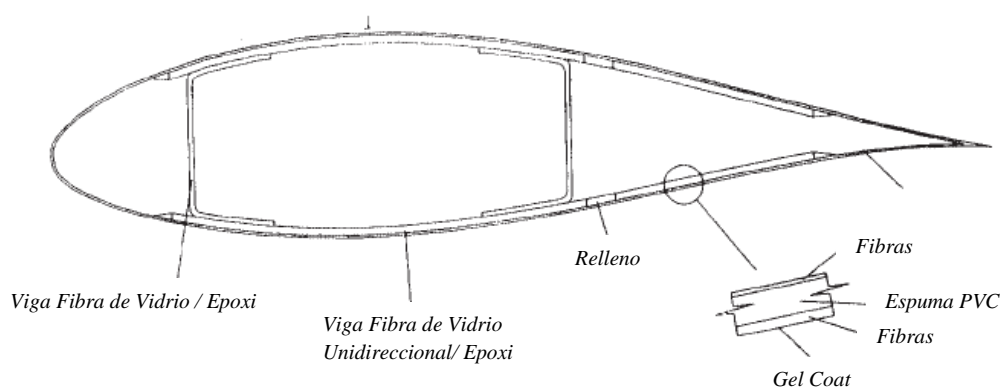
Estructura de concha reforzada con doble viga de fibra de vidrio.
